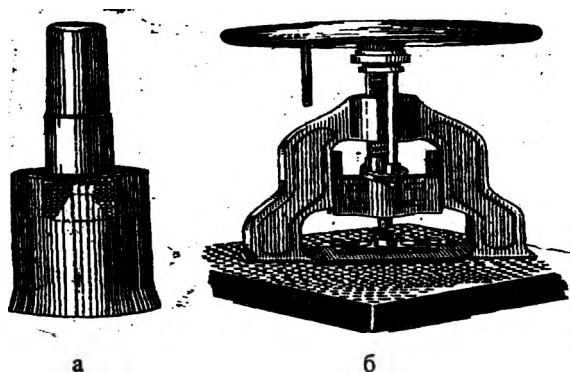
Аппараты для наружной штамповки: а) аппарат Паркера; б) пресс для штамповки
